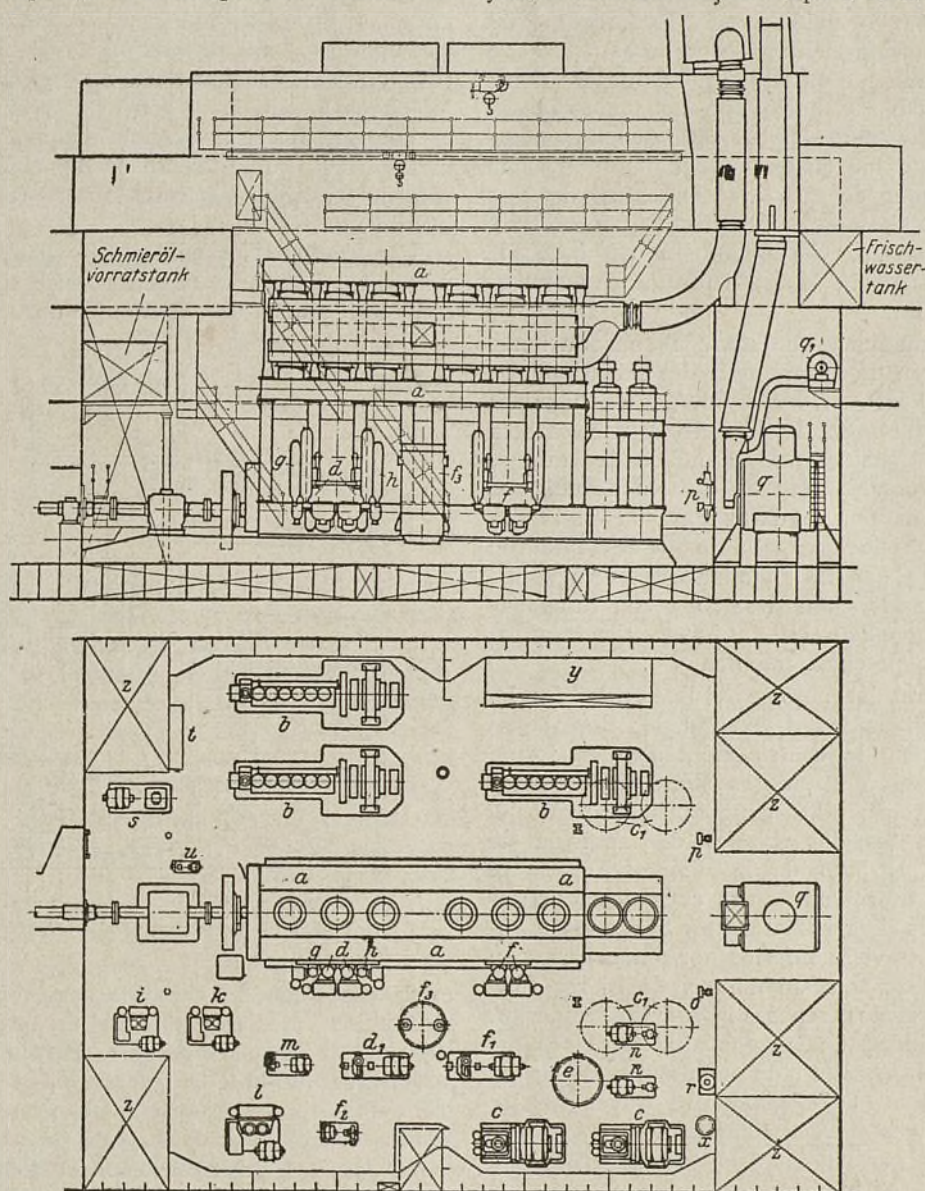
Disposición de la sala de Máquinas del «Magdeburg»
